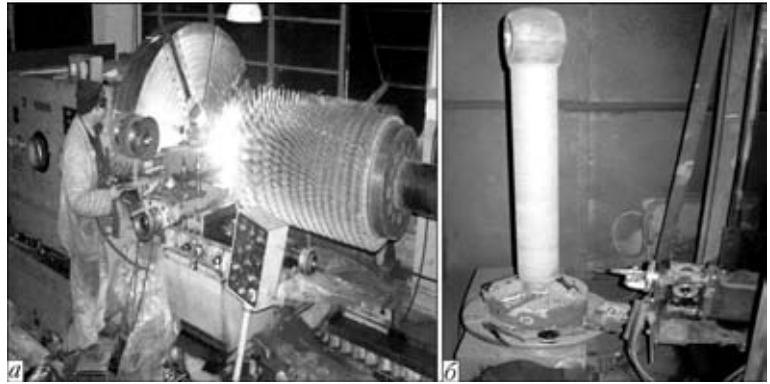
Напыление покрытия на опорную шейку вала турбины (а) и штока гидроцилиндра (б)
